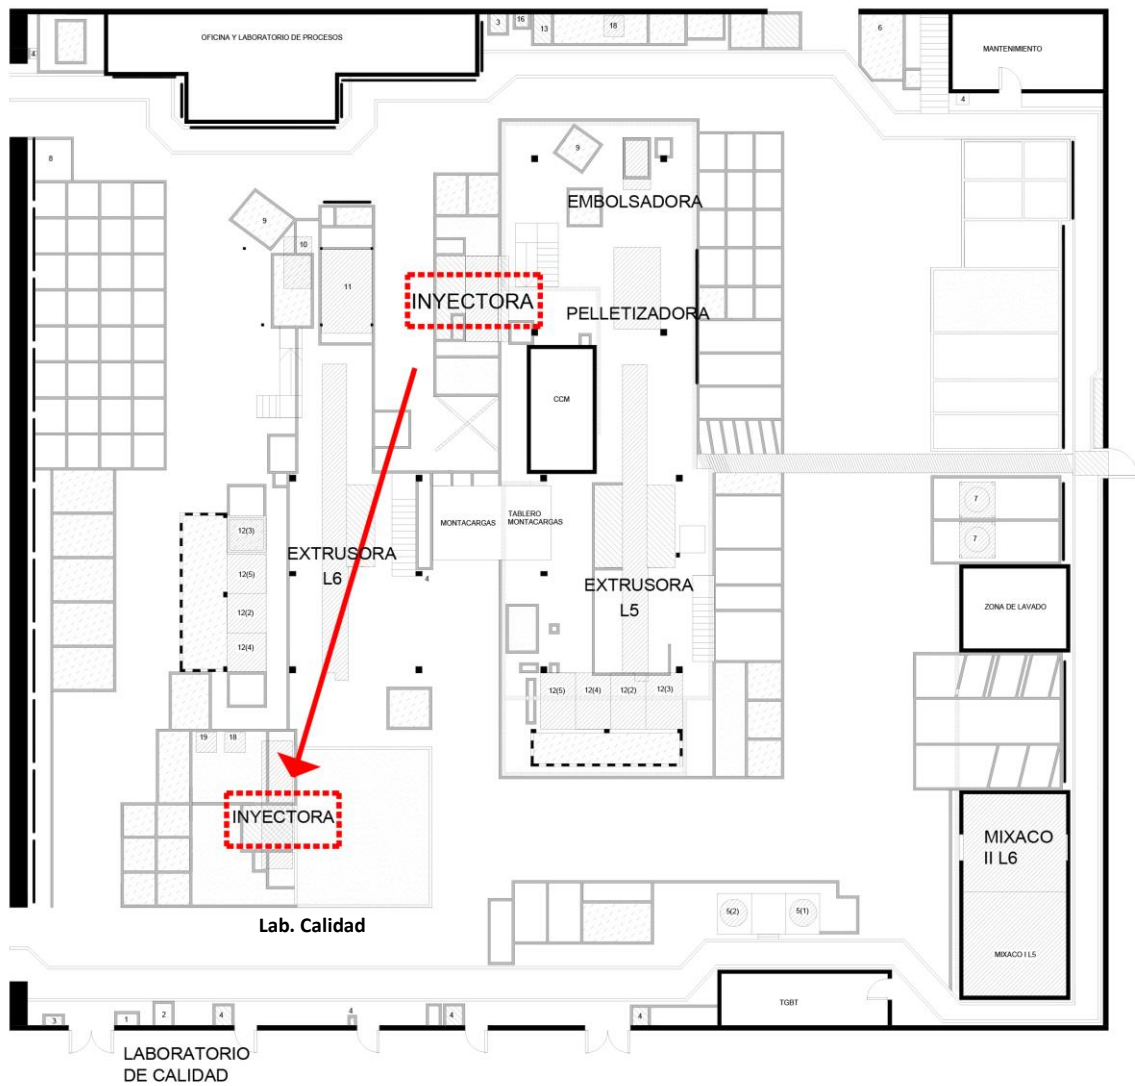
Layout con movimiento de máquina inyectora realizado en planta
